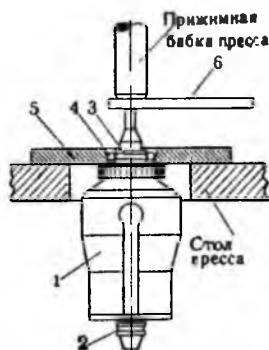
Приспособление для выпрессовки внутренних колец шарикоподшипников магнето СС-4 на прессе.
